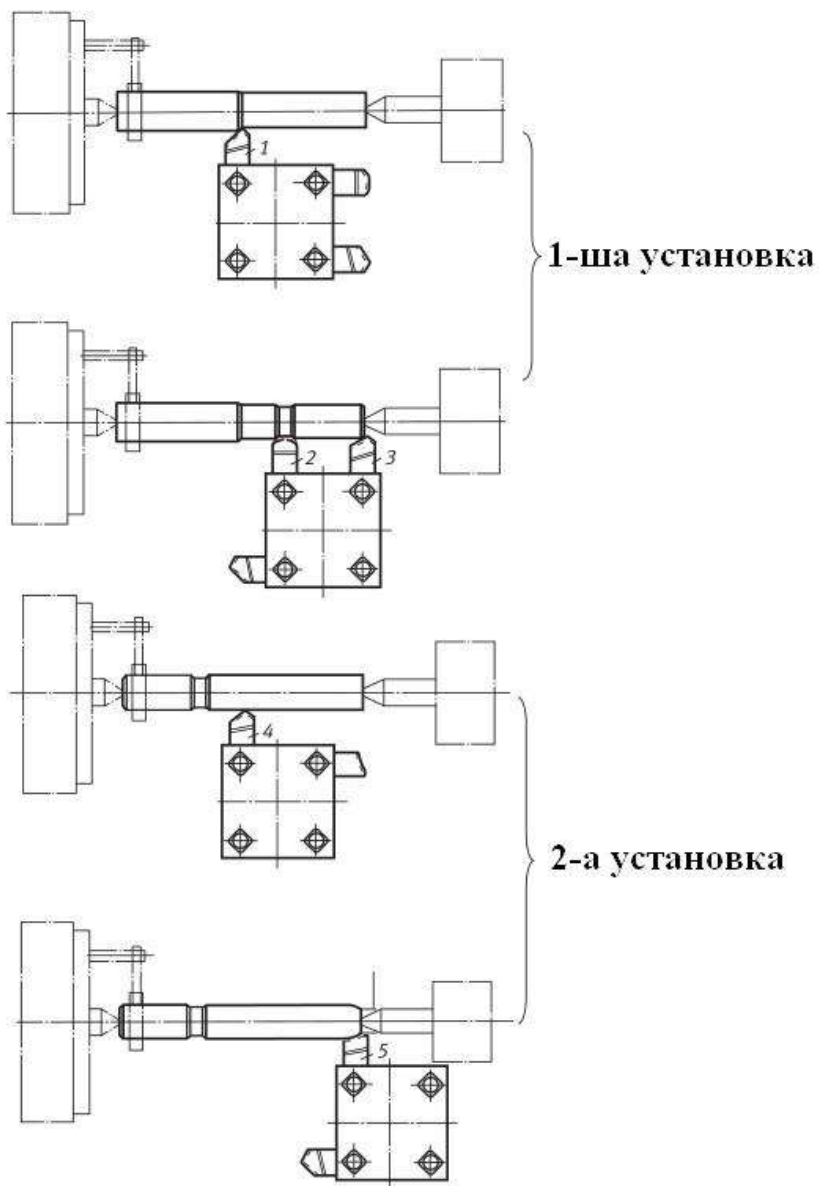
Обробка вала на токарному верстаті у дві установки.
